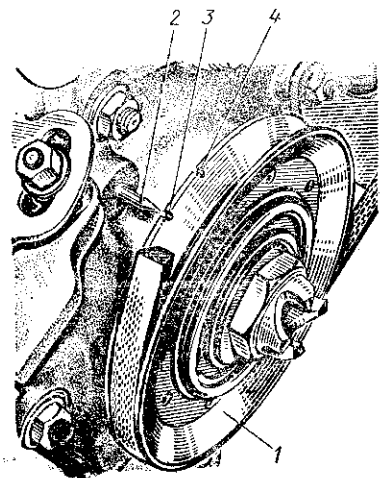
Установочные метки на ободе ведущего шкива коленчатого вала:
